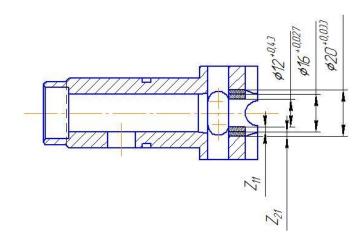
Эскиз диаметрального припуска для размера 18
